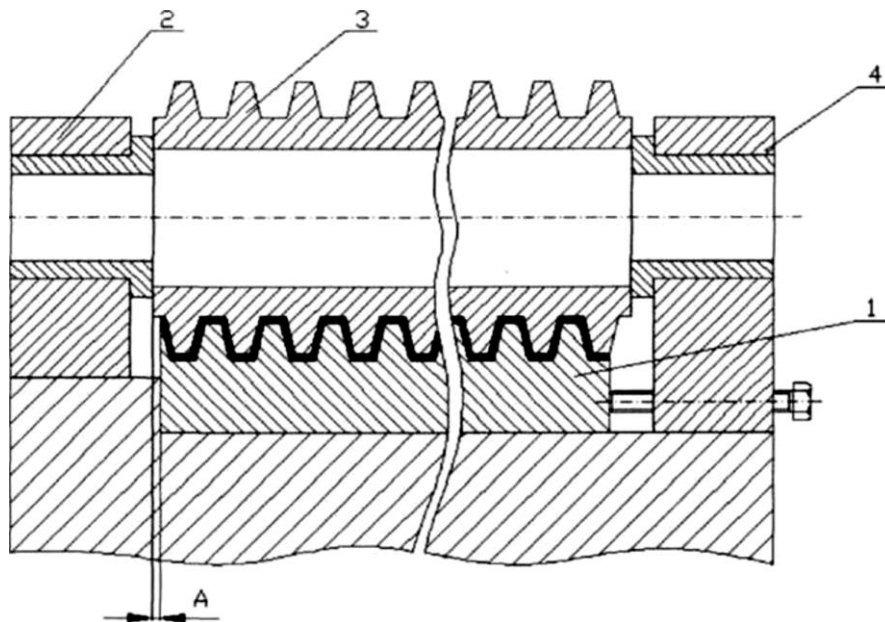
Схема формування робочих поверхонь профілю рейок за допомогою самозатверджувальних пластмас: 1 – рейка; 2,4 – опори; 3 – майстер-черв'як
